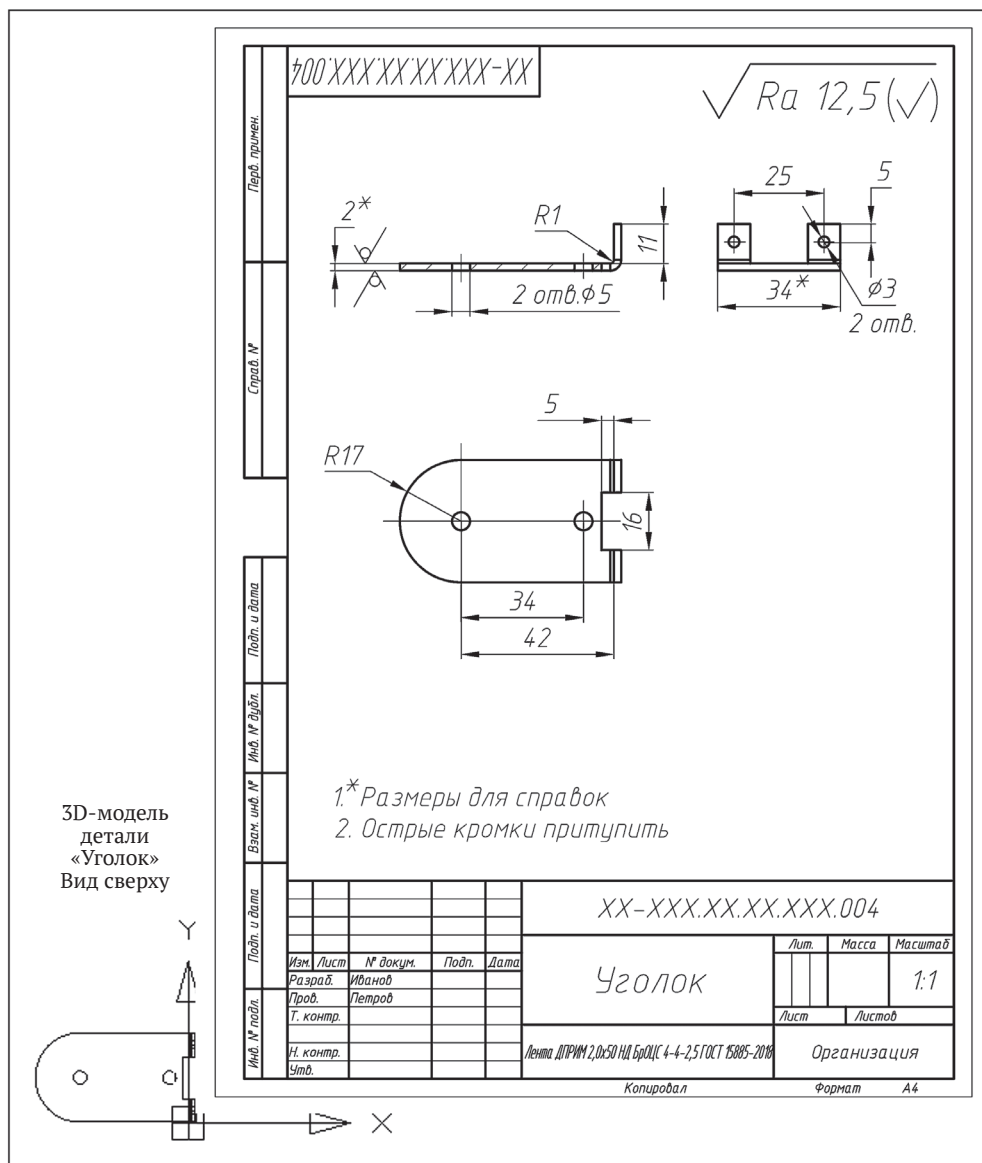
Пример выполнения чертежа детали «Уголок» до внесения изменений в размеры ее 3D-модели
